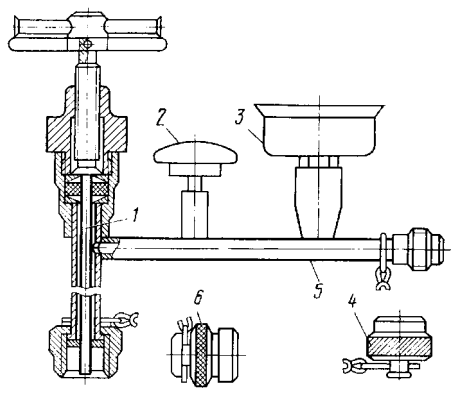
Приспособление для проверки давления и зарядки амортизатора шасси:
